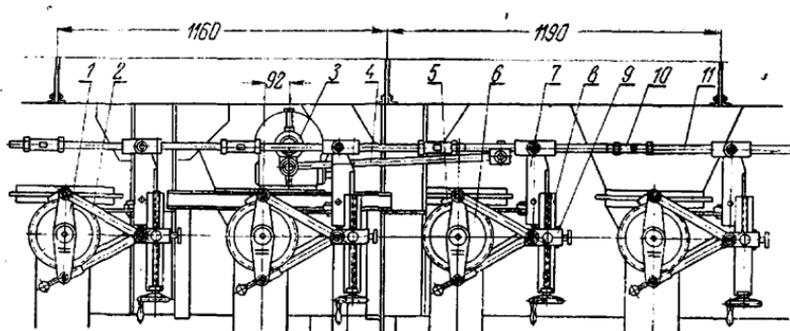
Приводной механизм дозаторов комбикормового агрегата МУКЗ-50.
